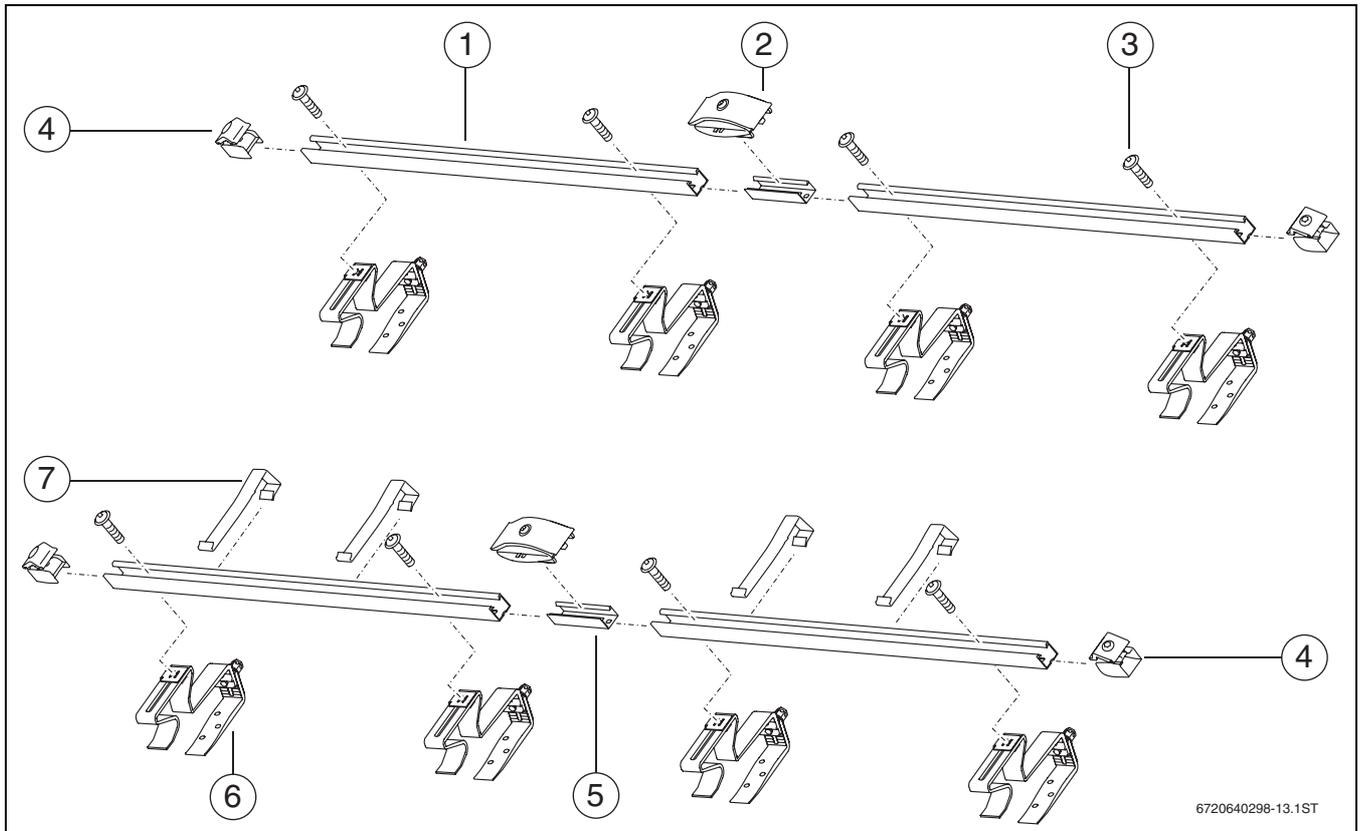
Montage-Set für 2 Kollektoren: 1 Montage-Set Grundausführung, 1 Montage-Set Erweiterung und 2 Montage-Sets für Dachziegel
